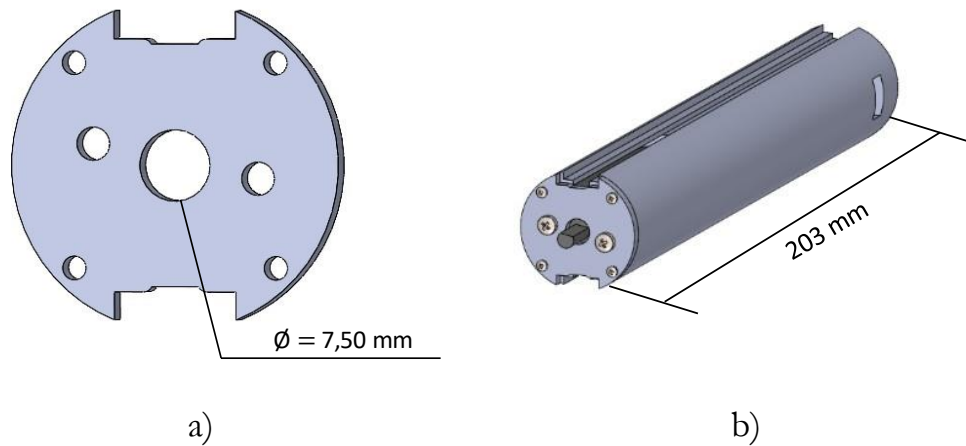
Tampa do motor: a) vista frontal, b) vista com montagem.
